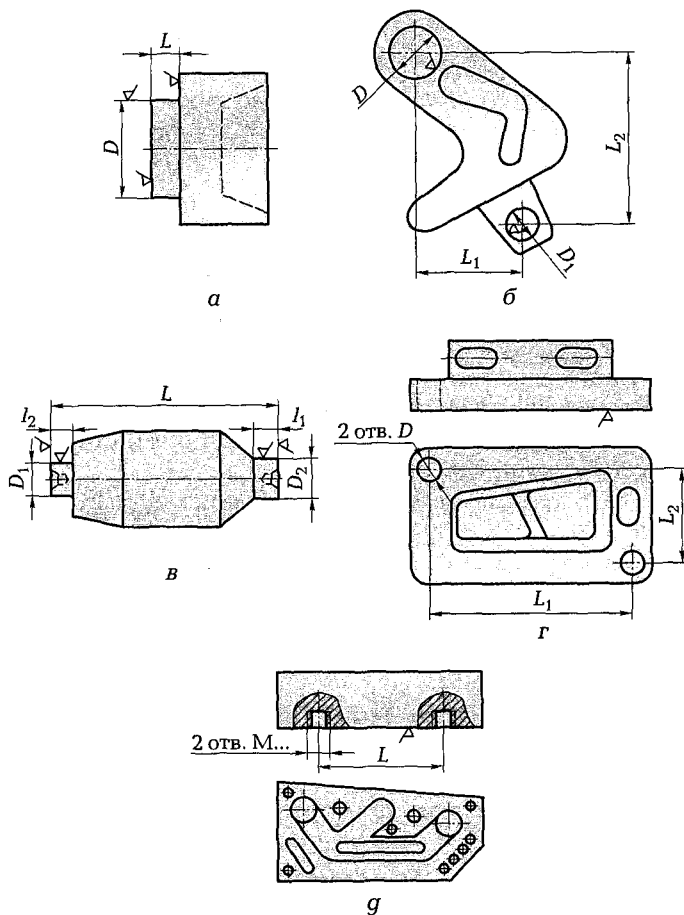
Примеры заготовок с базовыми поверхностями, подготовленными для обработки на станках с числовым программным управлением:
